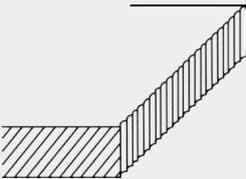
Importance du lissage d'un cordon de soudure.
